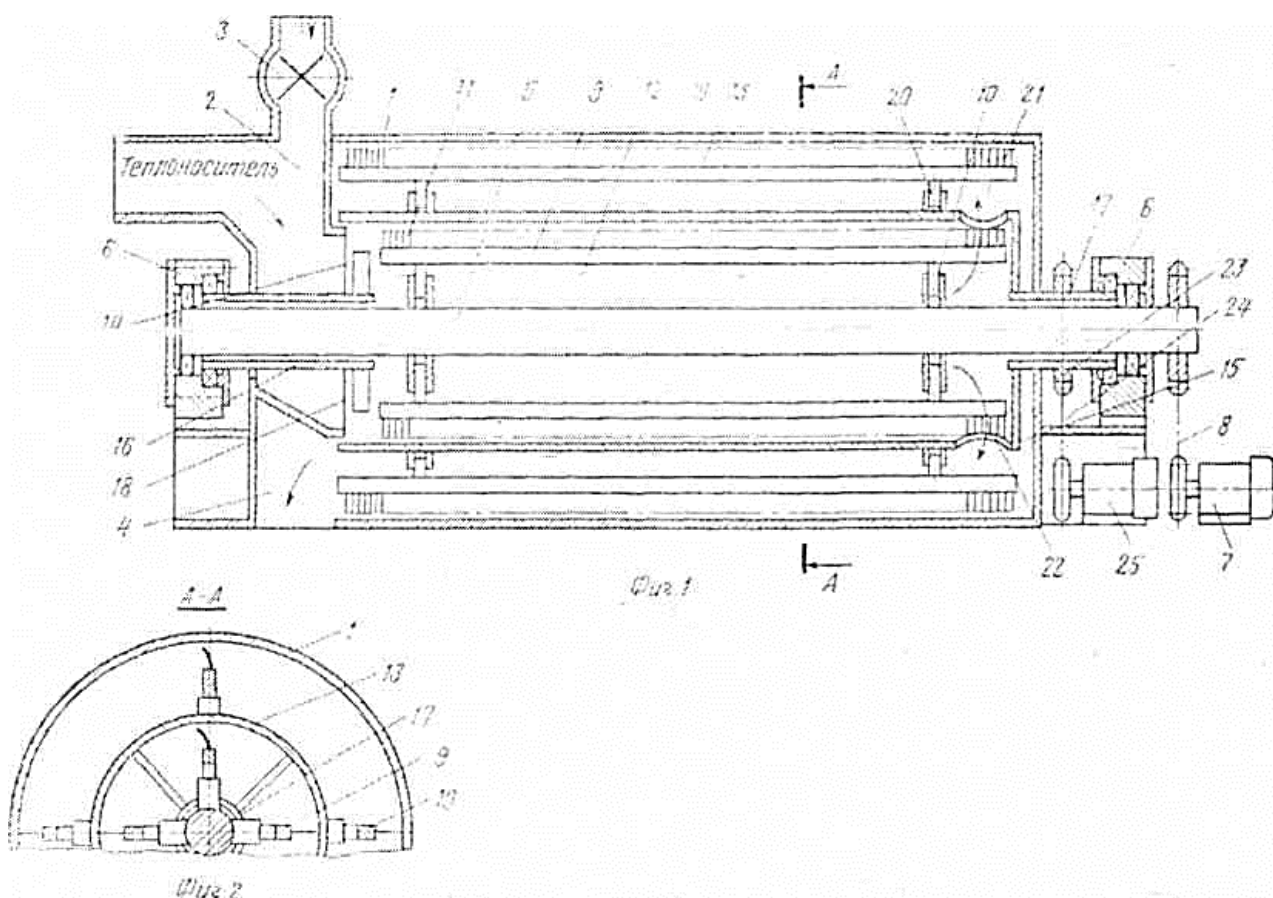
Установка для сушки сипких матеріалів: 1 – нерухомий корпус; 2 – патрубок для завантаження; 3 – шлюзовий затвор; 4 – патрубок для
